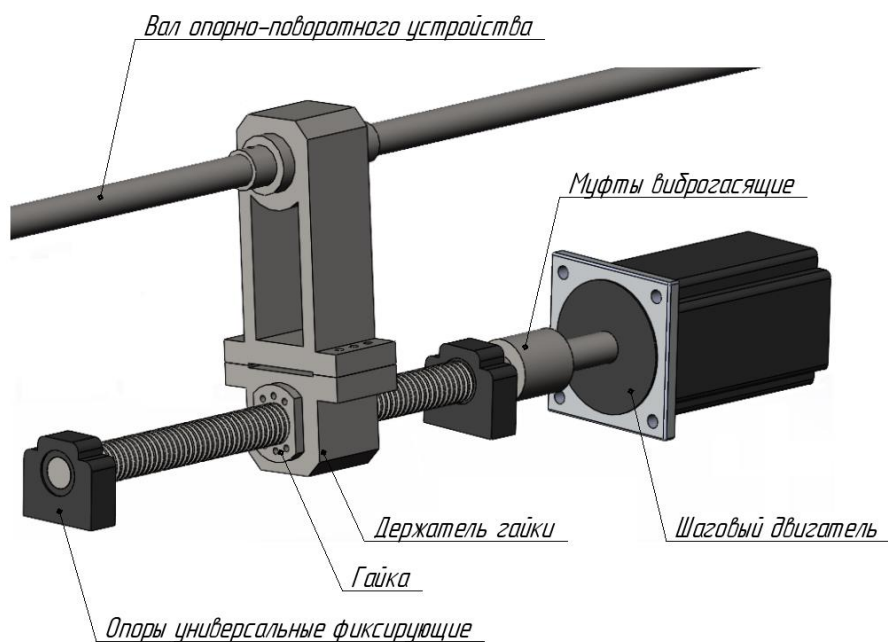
Общий вид механизма для передачи возвратно-поступательного движения
